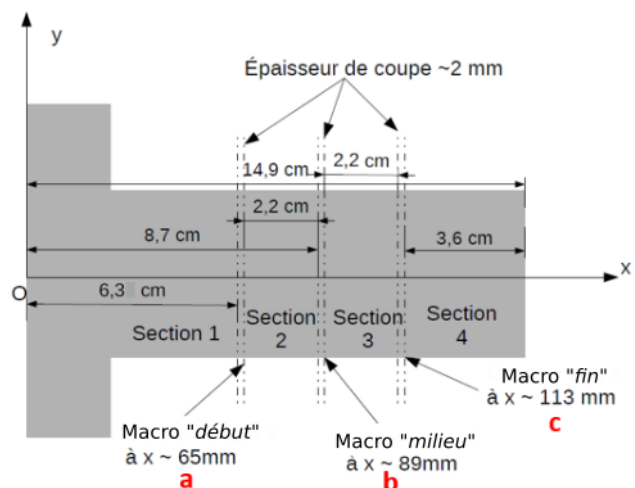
Emplacement des macrographies sur l'éprouvette.
